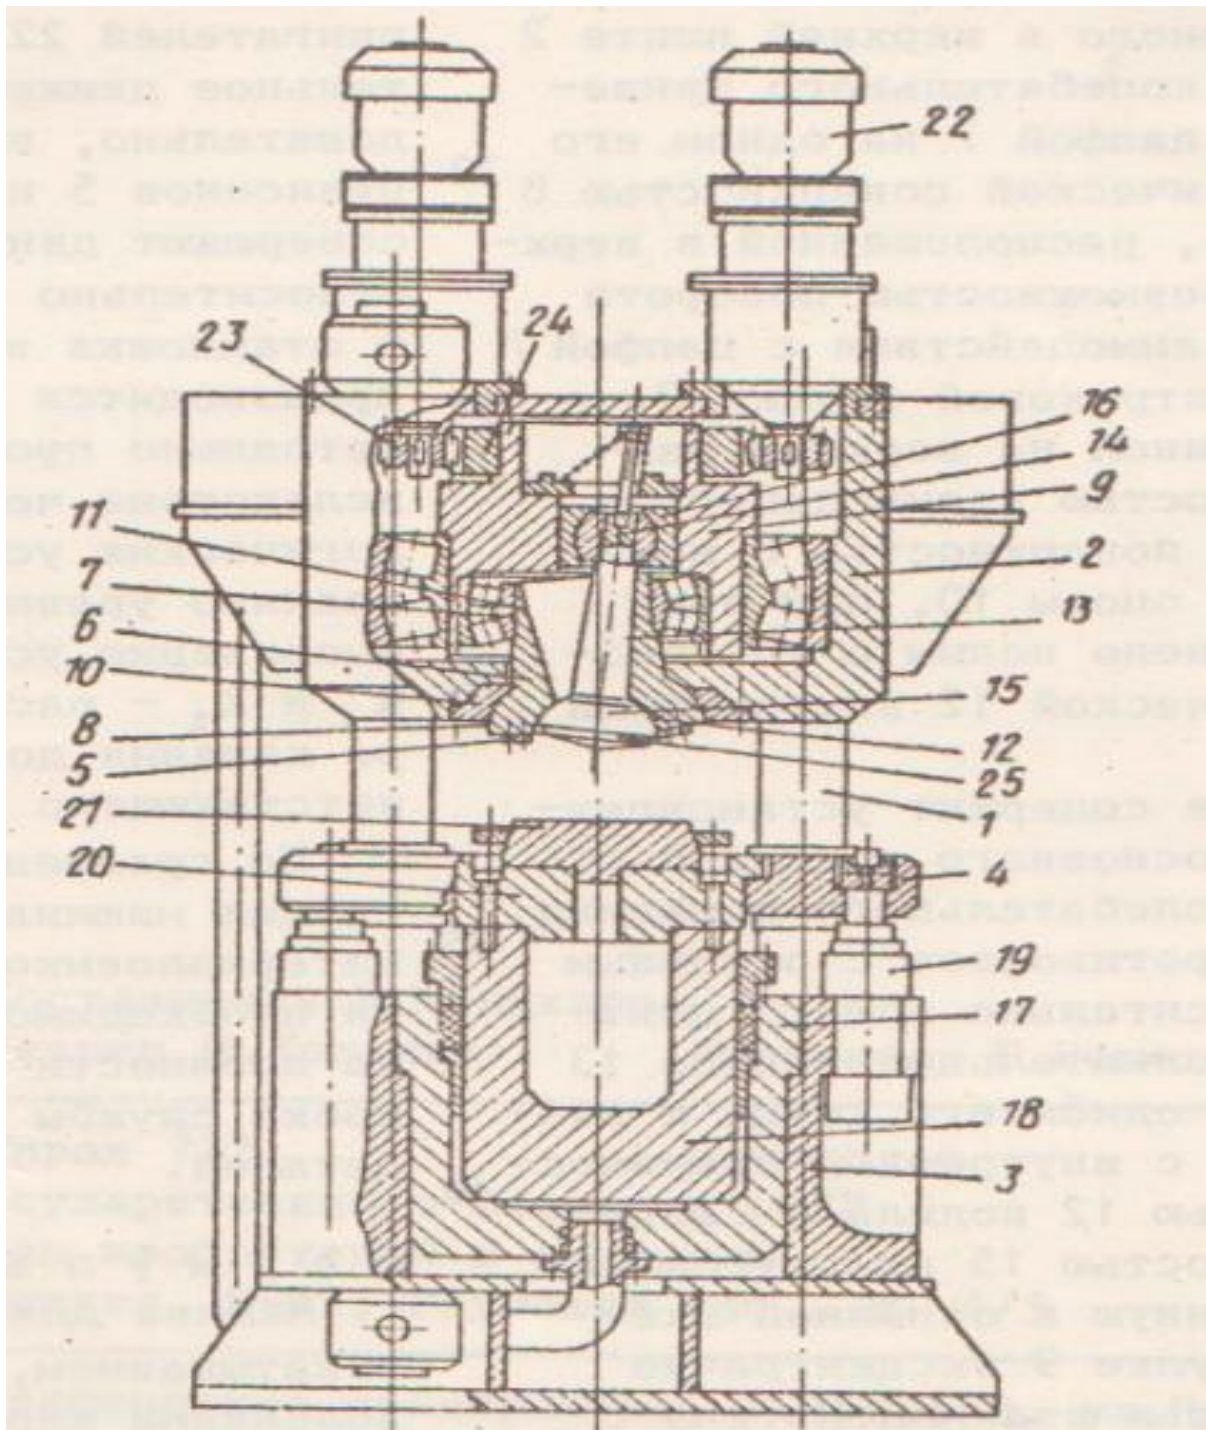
Машина для штампування заготовок обкатуванням [42].
